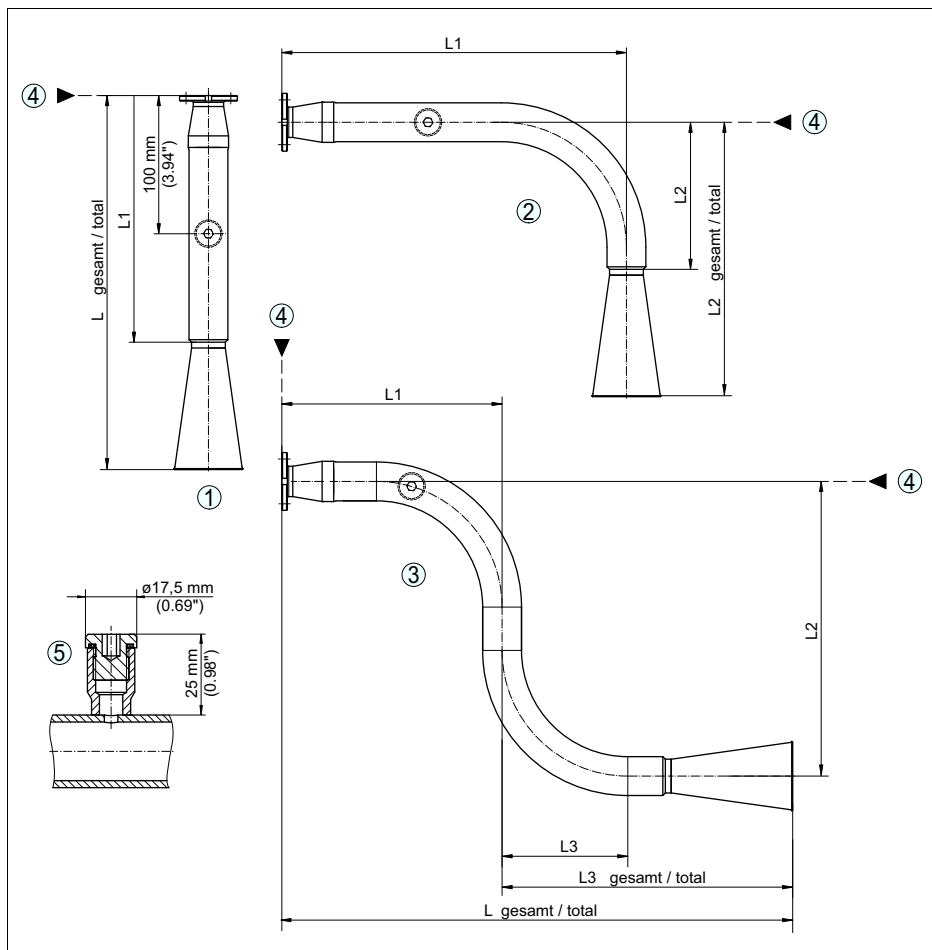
Prolongamento de um segmento, com antena tipo corneta soldada, medidas de acordo com as especificações da encomenda
